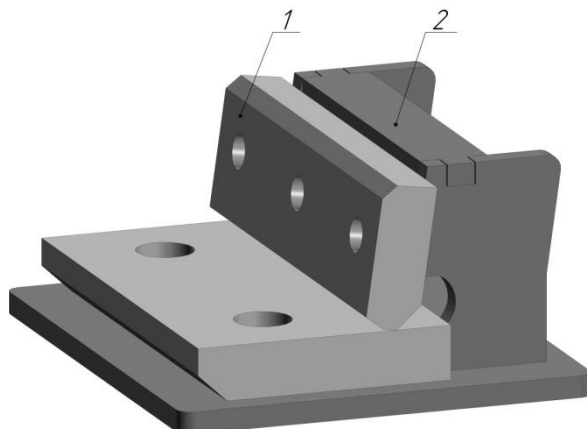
Приспособление для сборки и сварки держателя ножей
